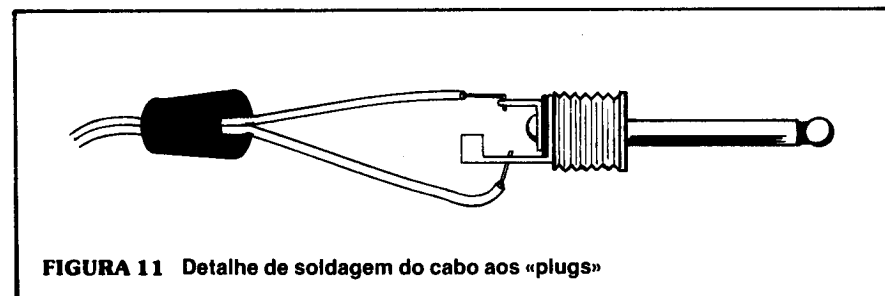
Detalhe de soldagem do cabo aos «plugs»
